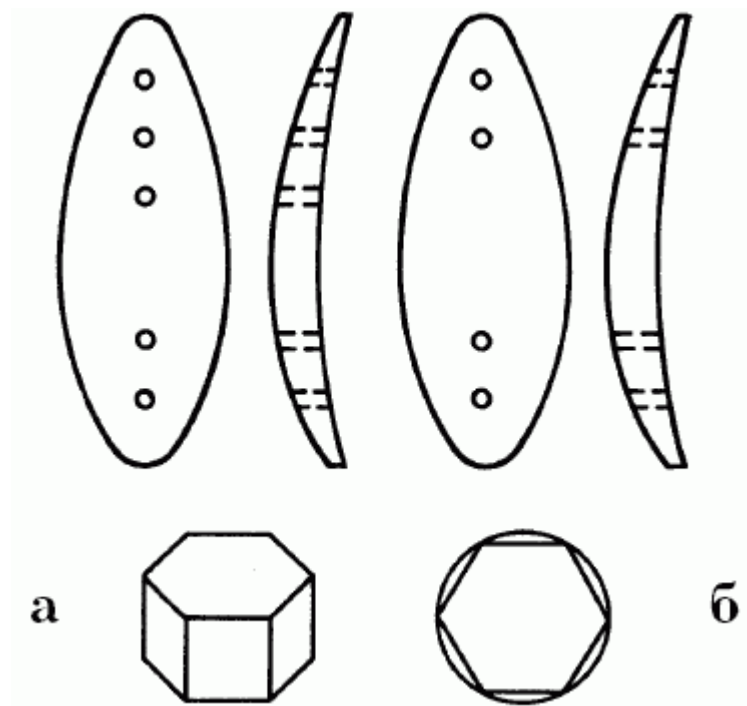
Точечная запрессовка стерженьков одного металла в заготовку блесны другого по заданным профилям: – варианты размещения стерженьков в теле
